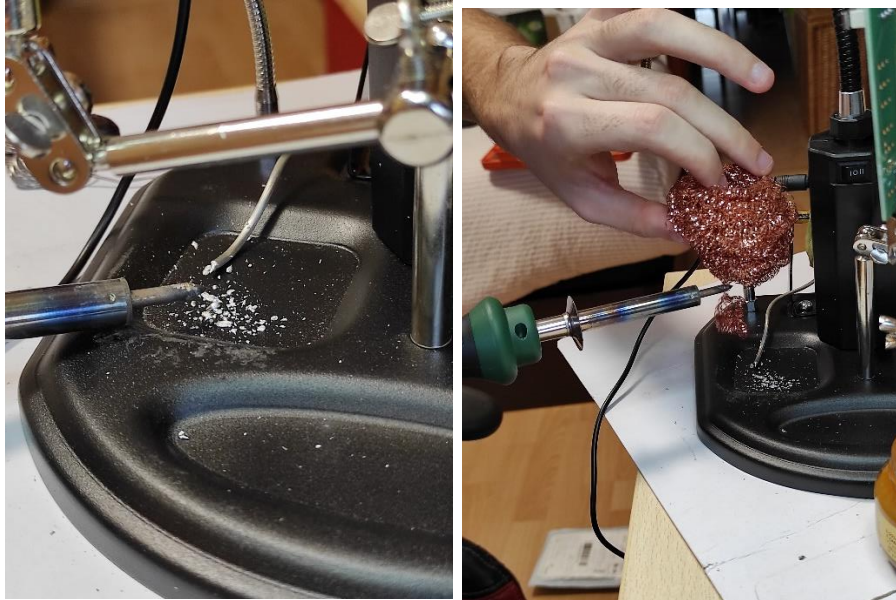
Soldadura dels pins dels components del *boosterpac*.
